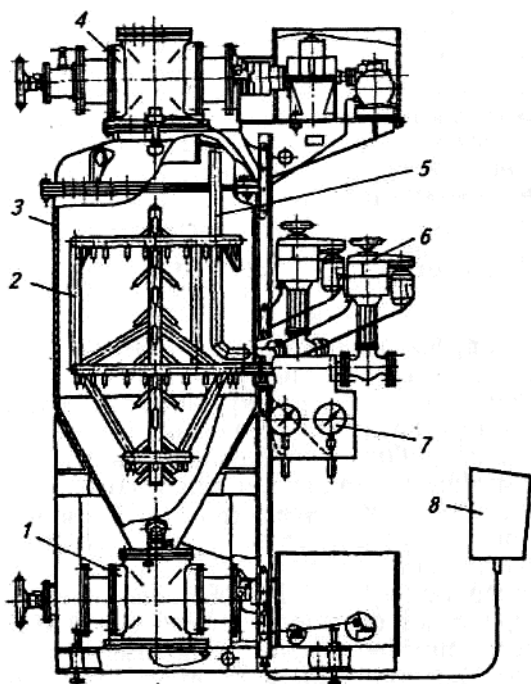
Аппарат А9-БПБ для пропаривания зерна крупяных культур: — разгрузочный затвор; 2— змеевик; 3— корпус; 4— загрузочный затвор; 5— колено; 6— вентиль; 7— манометр; 8— пульт управления
